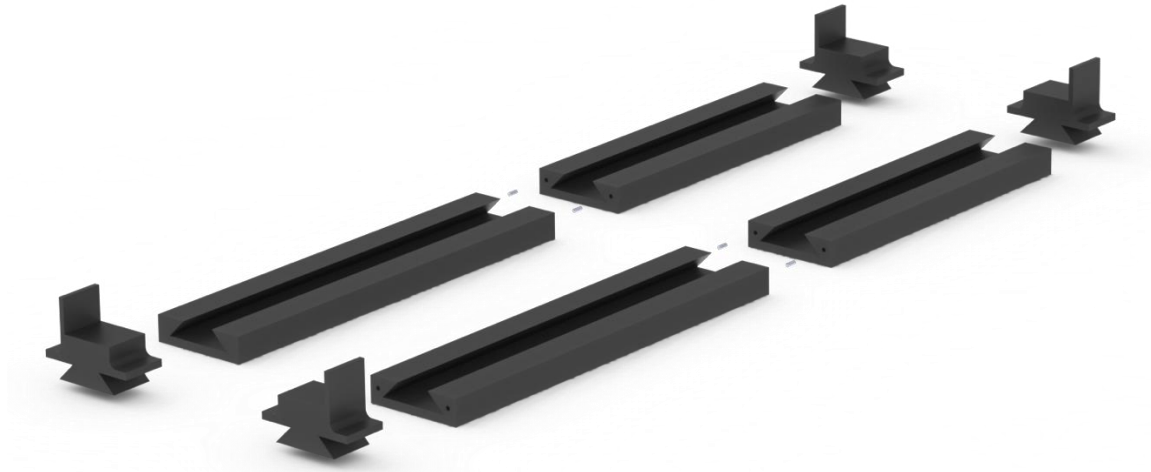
Vista explosionada del subconjunto 3. Fuente: propia
